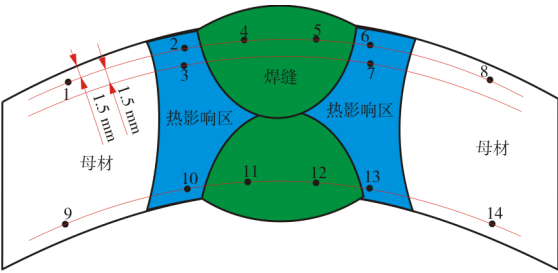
焊接接头维氏硬度试验压痕位置示意图
